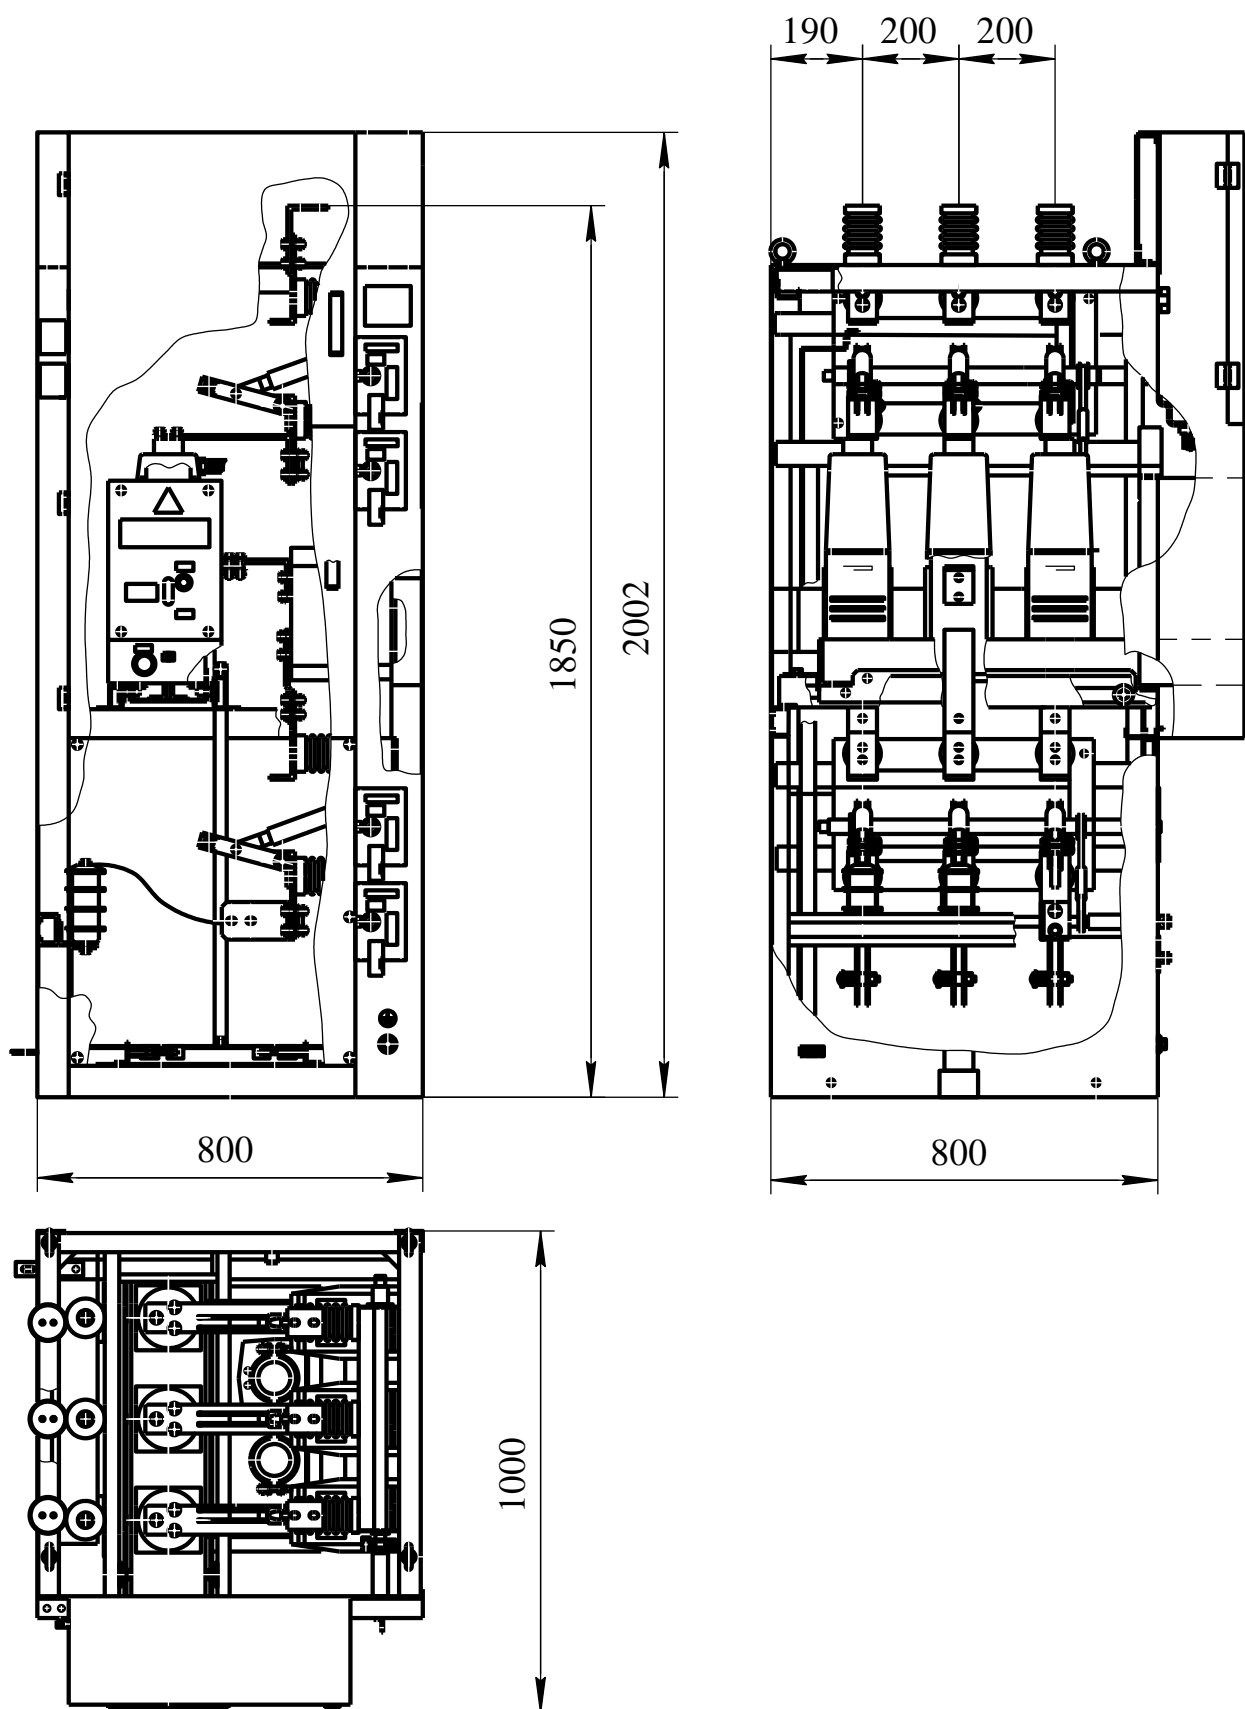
Габаритные размеры камер КСО типа КСО-306-(101-104)
